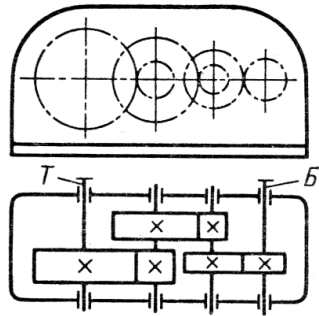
Горизонтальная развернутая схема трехступенчатого цилиндрического редуктора (ЦЗ)
